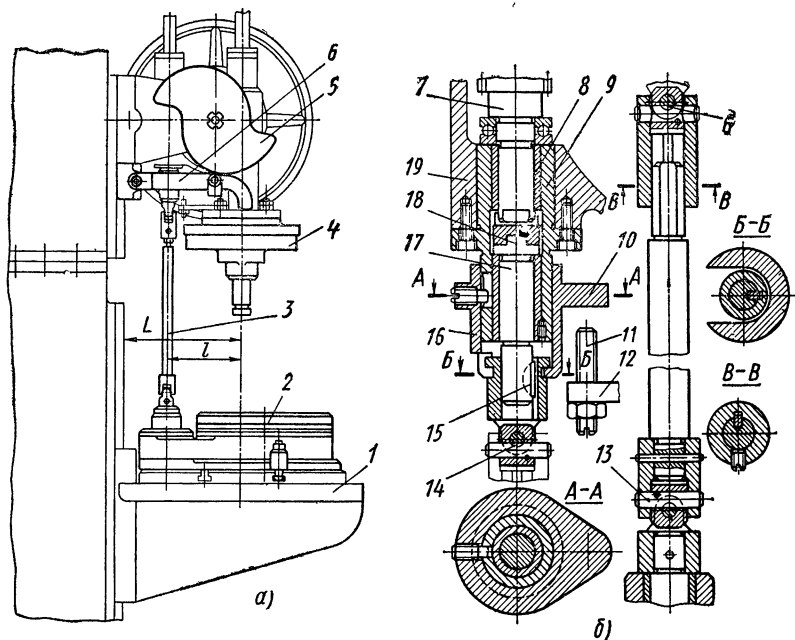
Механизмы, связывающие поворотный стол с приводом подачи шпинделя станка
